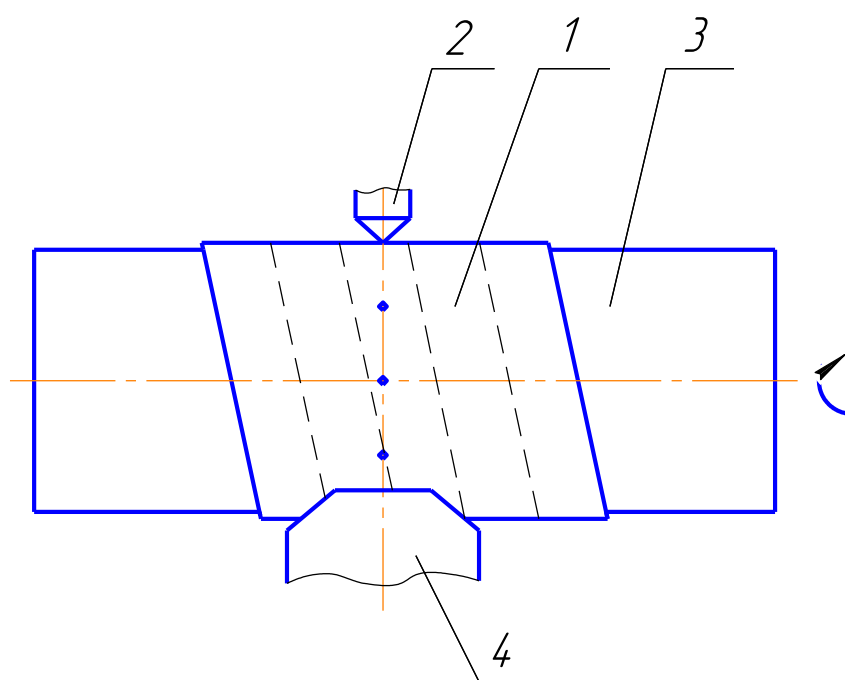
Схема определения твердости поверхности: 1- покрытие; 2- алмазный наконечник твердомера; 3 – образец ;4 – стол – призма твердомера.
